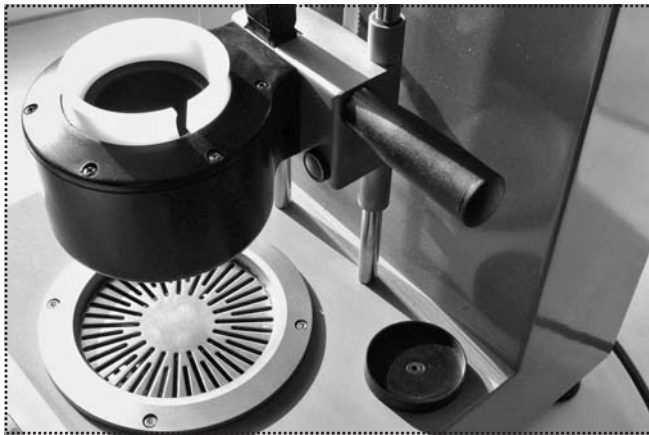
Установка ТВЧ для сборки фрез с термопатронами
